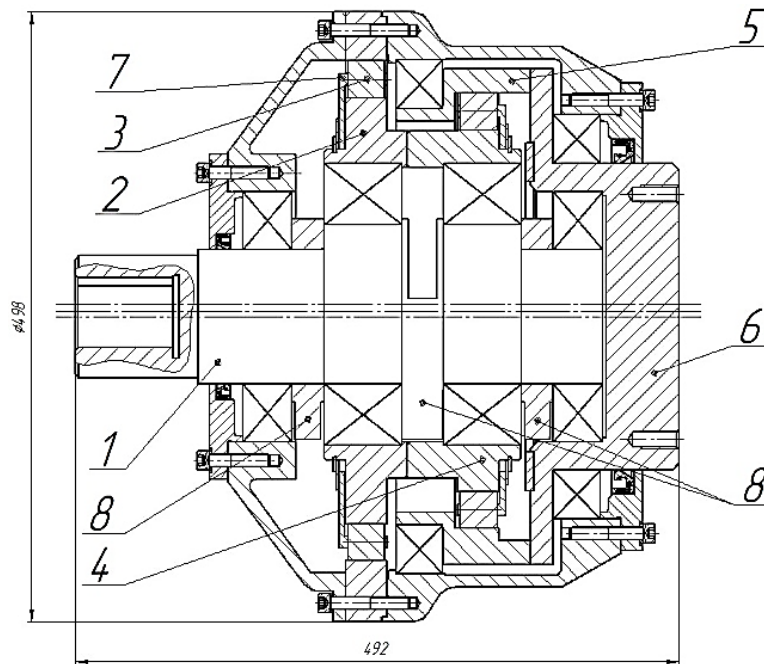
Компонка привода на базе передачи ПТКиСО: 1) генератор; 2) кулачек; 3) венец; 4) кулачек; 5) венец; 6) выходной вал; 7) сепаратор; 8) противовесы
